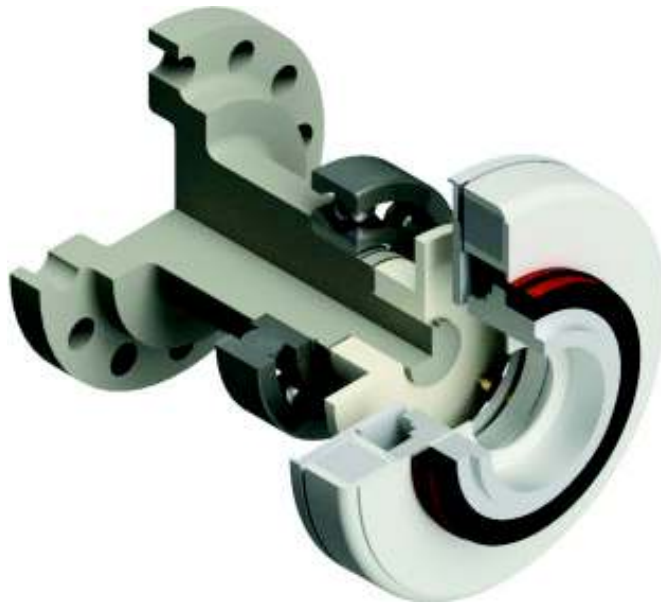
Corte isométrico del sistema de integración del rotor de la máquina sincrónica y el motor de arranque
